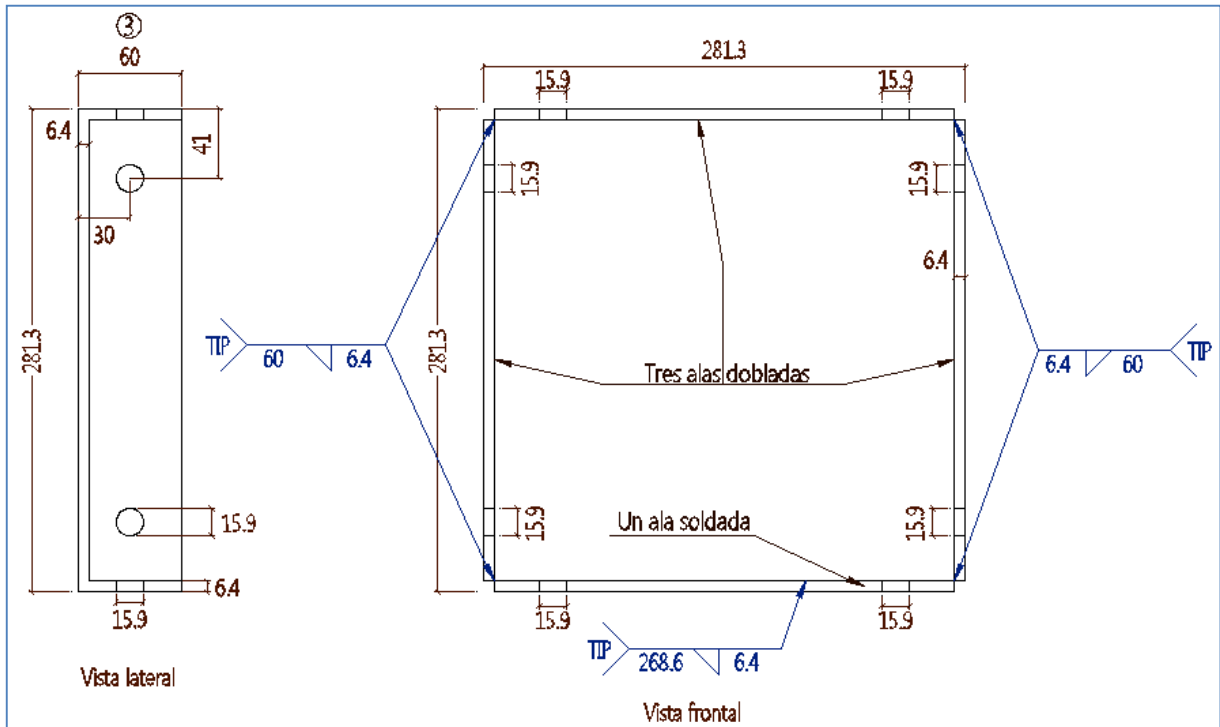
Detalle despiece pieza No.3 modelo 2 tensión.
